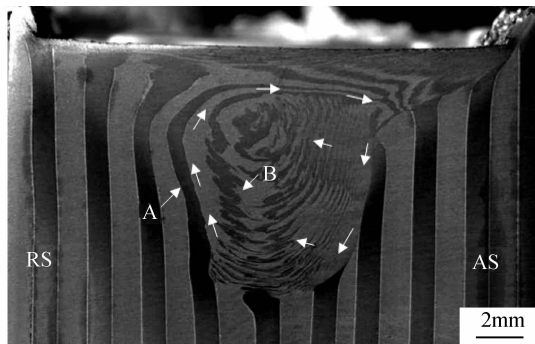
平行焊缝排列横截面上材料流动宏观形貌
